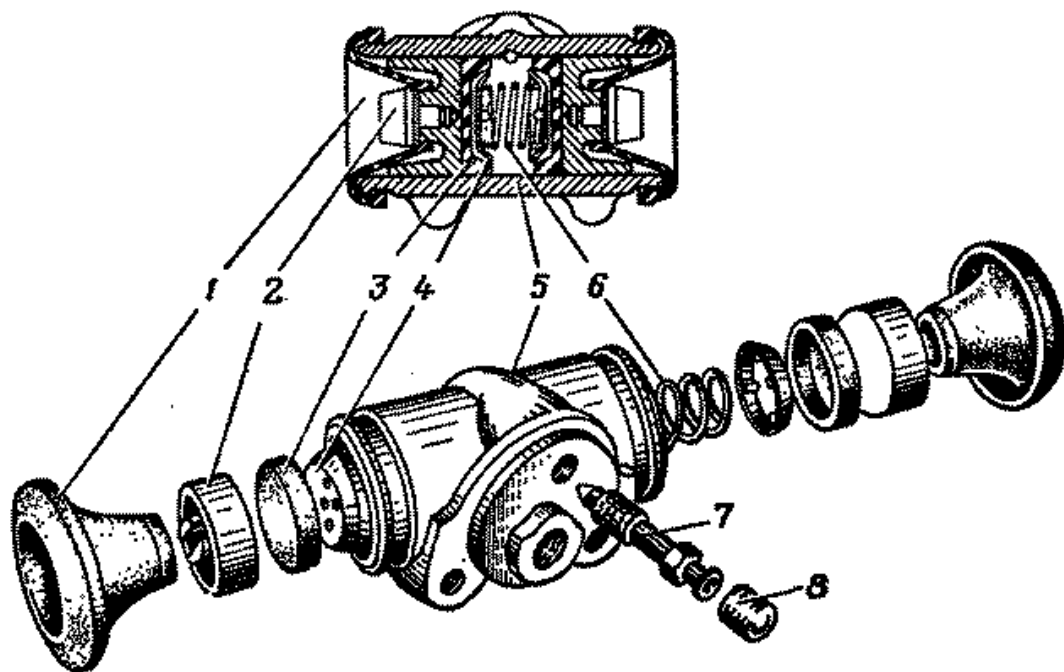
Цилиндр колесный заднего тормоза в сборе:
